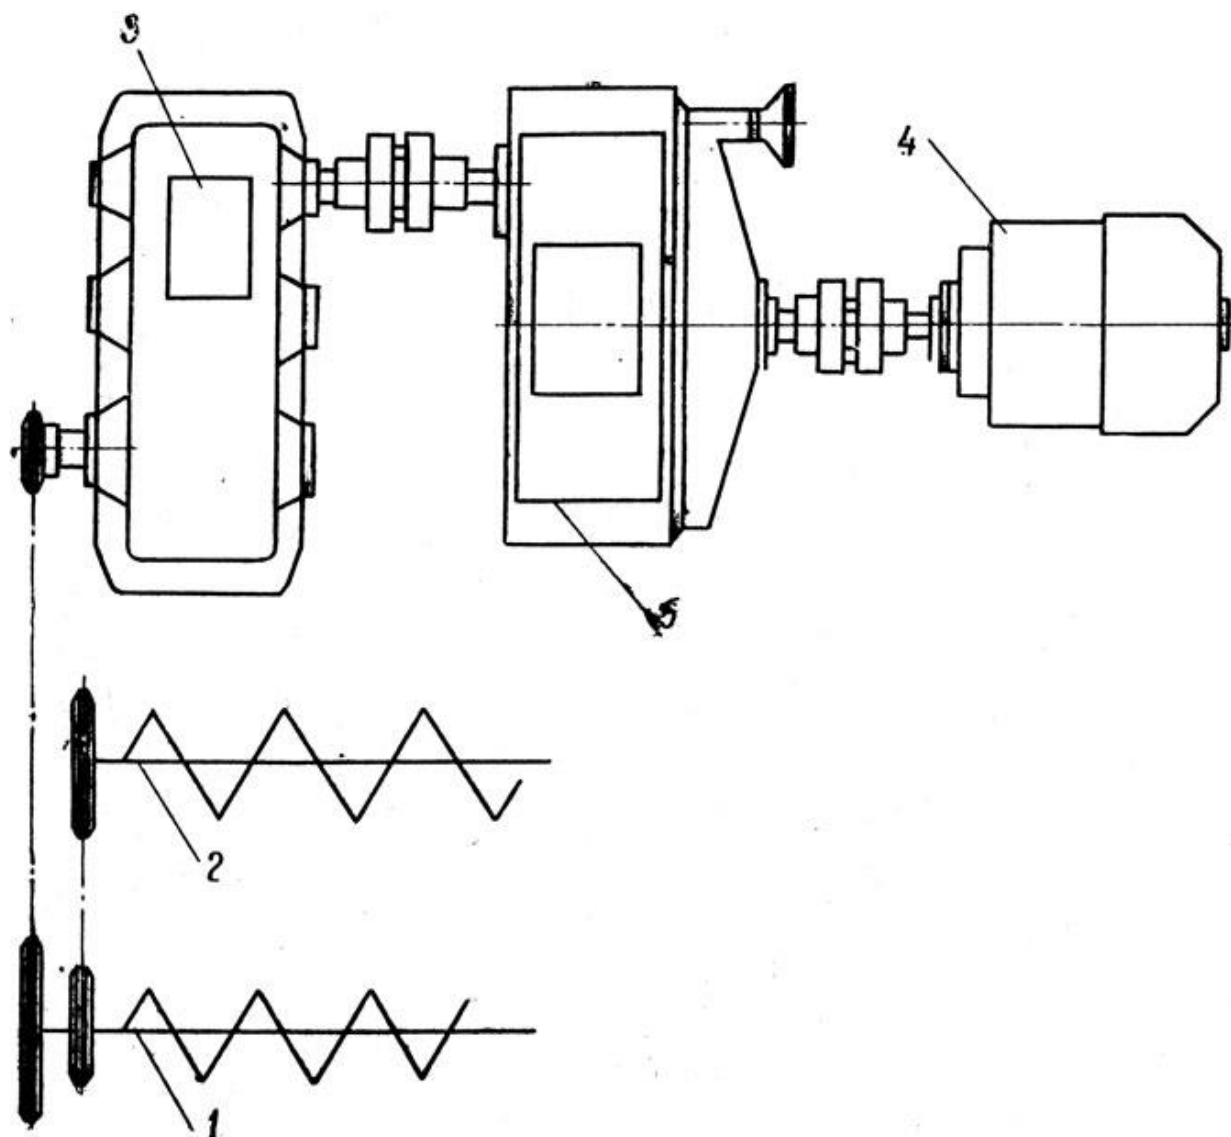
Схема привода одношнекового пресса и варильника марки А1-ИВБ: 1 - вал пресса; 2 - вал варильника; 3 - редуктор ЦДН - 35; 4 - электродвигатель; 5 - вариатор
